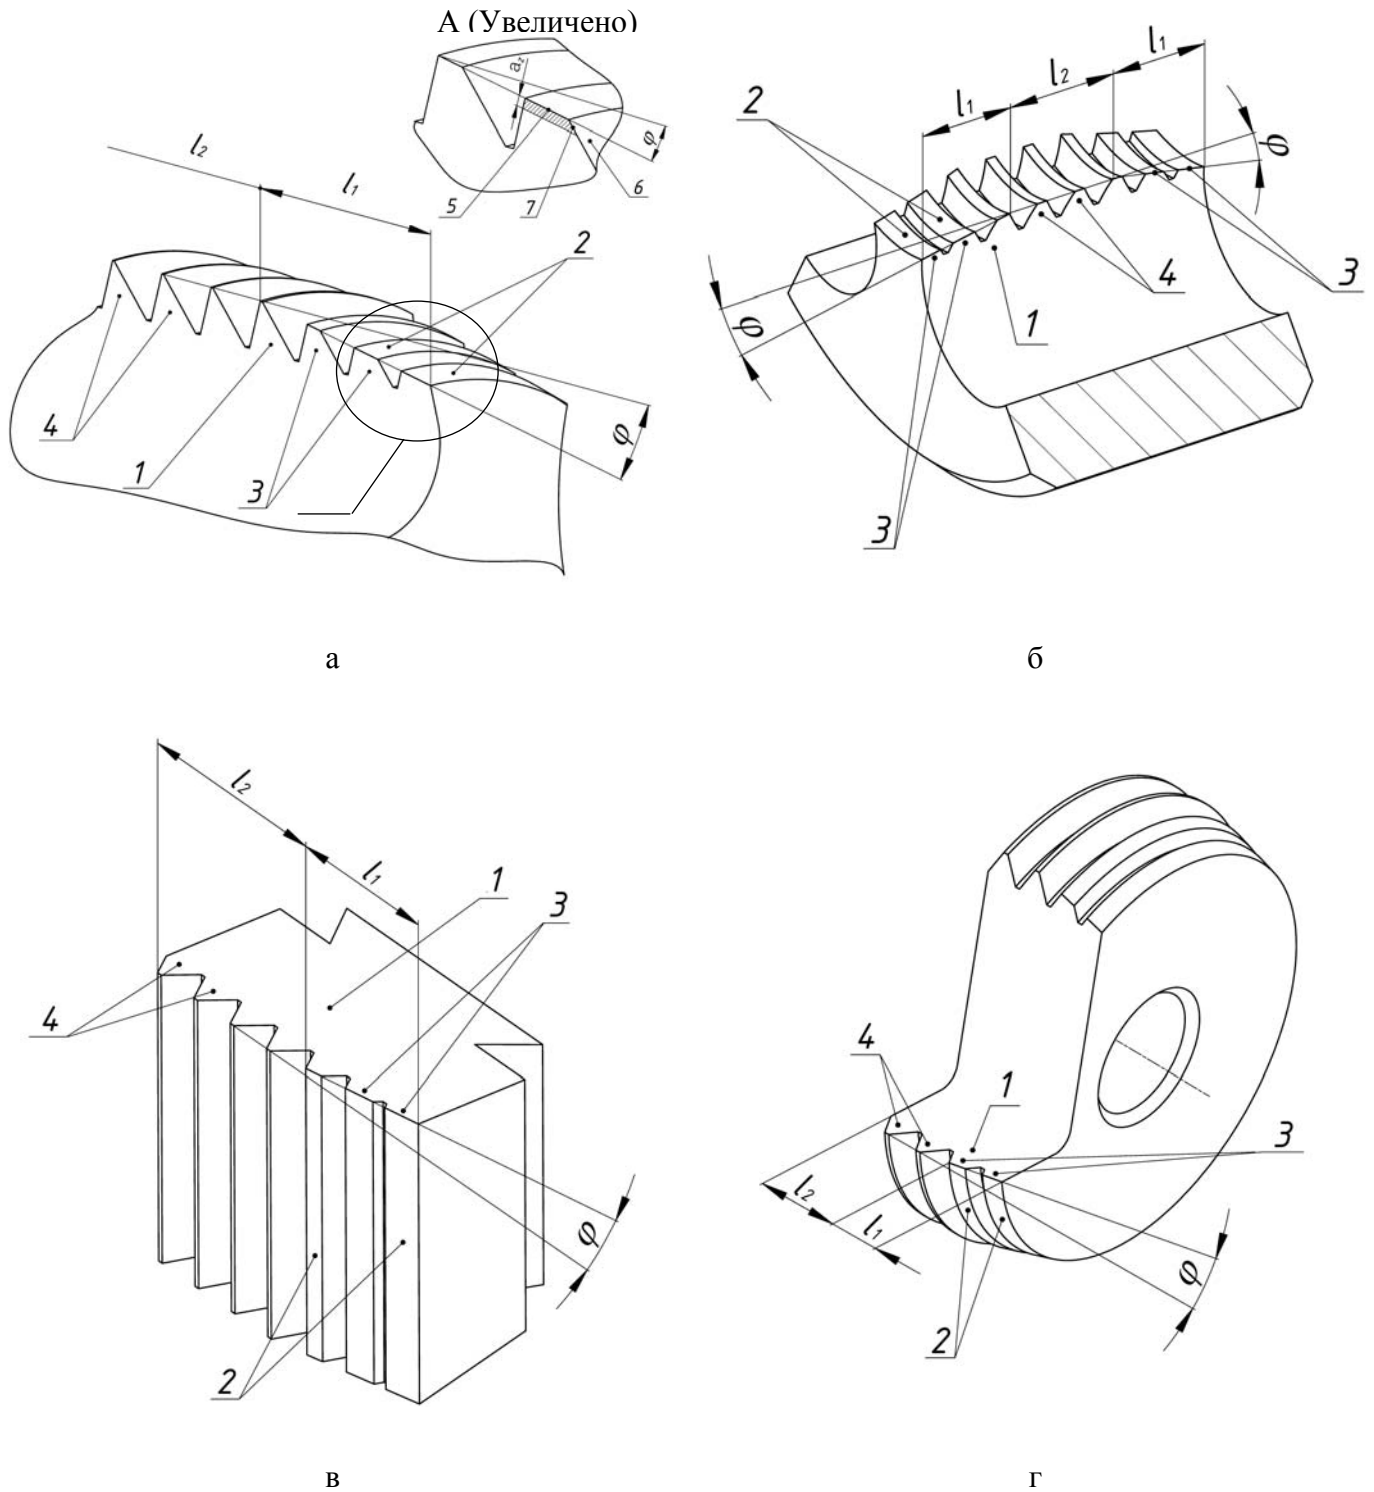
Основные конструктивные элементы, поверхности и режущие кромки рабочей части резьбонарезного инструмента: а - метчик, б - плашка, в - призматическая резьбовая гребенка, г - круглая резьбовая гребенка
